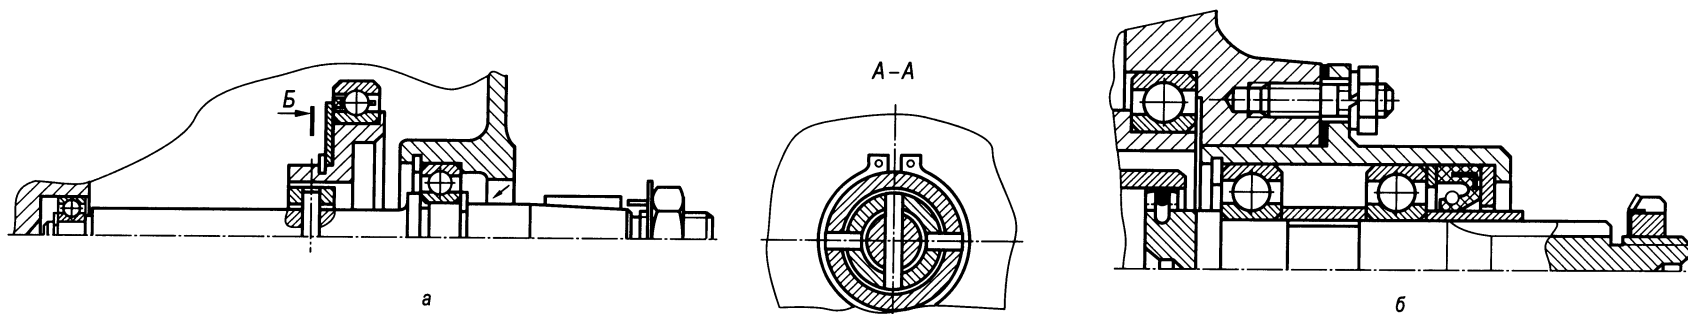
Входной вал волнового (а) и планетарного (б) зубчатого редуктора
